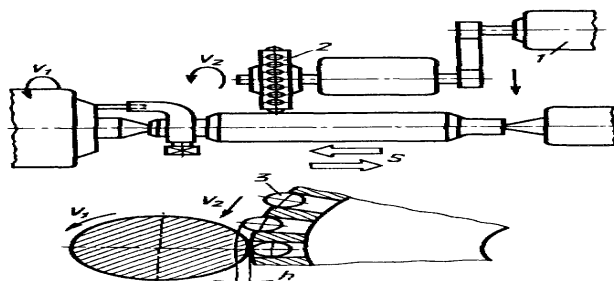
Схема ударного накатування поверхні деталі: 1 - сепаратор; 2 - привід обертання сепаратора з кульками, 3 - сталева кулька;  $V_1$  - обертання деталі;  $V_2$  - обертання сепаратора;  $h$  - діапазон вільного коливання кульки в сепараторі
